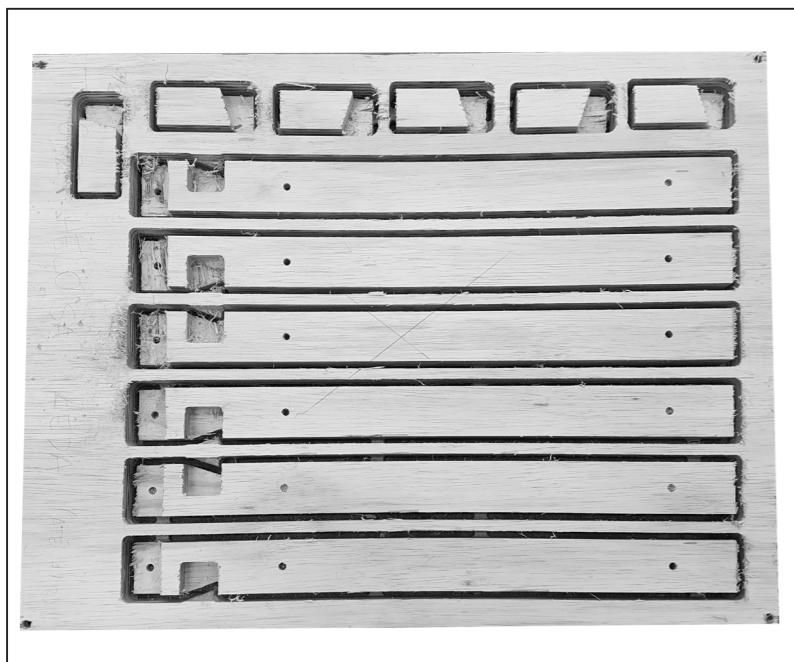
Placa cortada na fresa CNC, com as peças das pernas.
